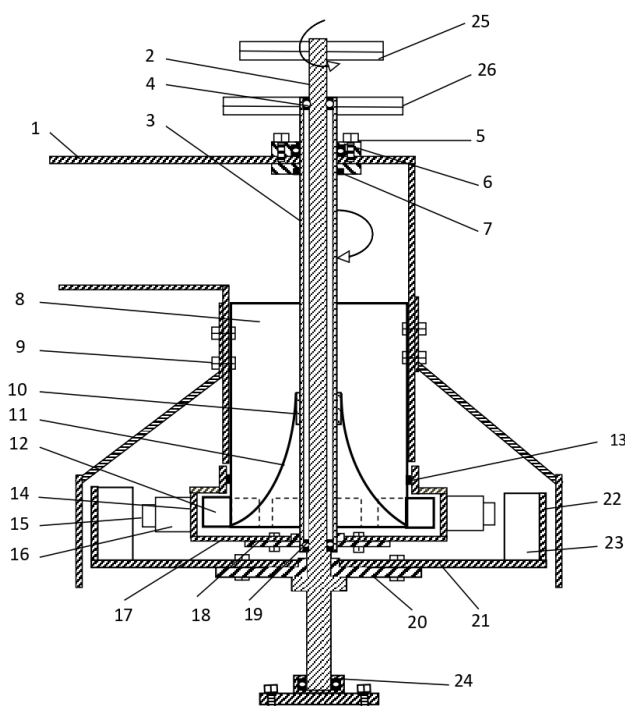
Общий схематический вид контрроторного гидравлического агрегата. Активное рабочее колесо передает вращательное движение отдельно установленному генератору через шкив 25, закрепленный на внутреннем валу. Вращательное движение
